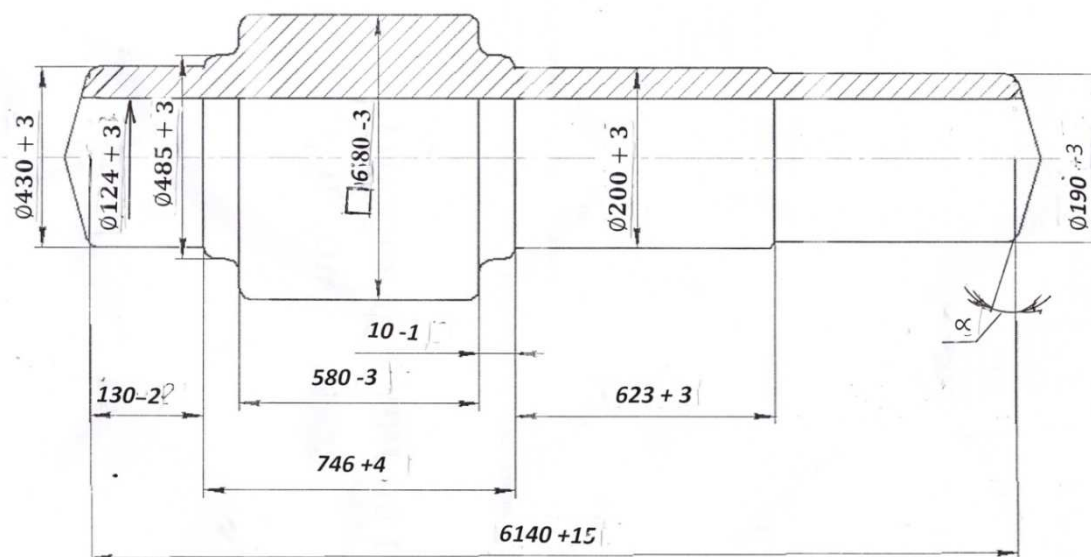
Вид пустотелой заготовки, заготовки, полученной из проката квадратного сечения
